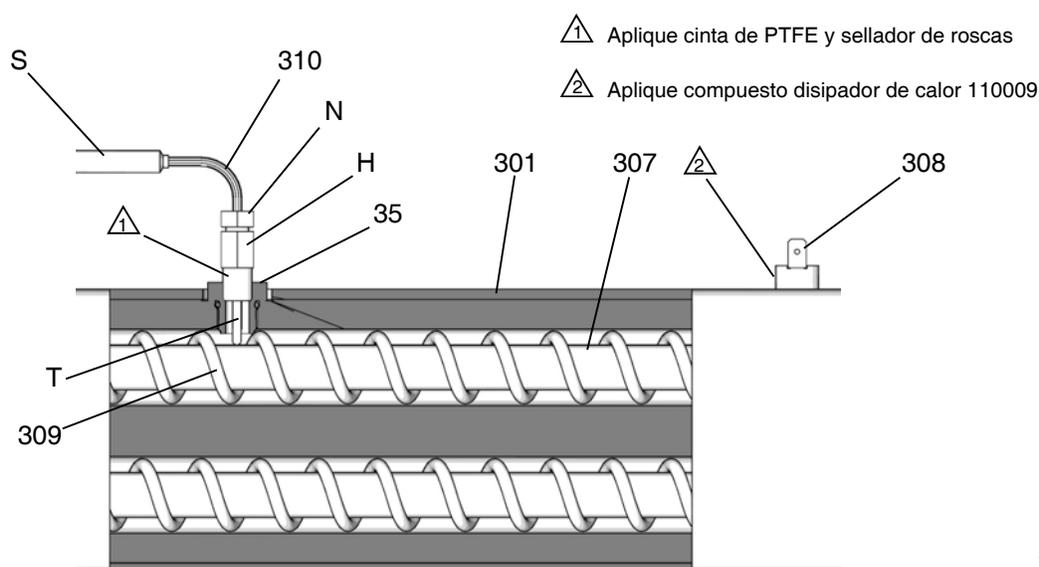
Calentador (se muestra calentador de zona única de 7,5 kW)
